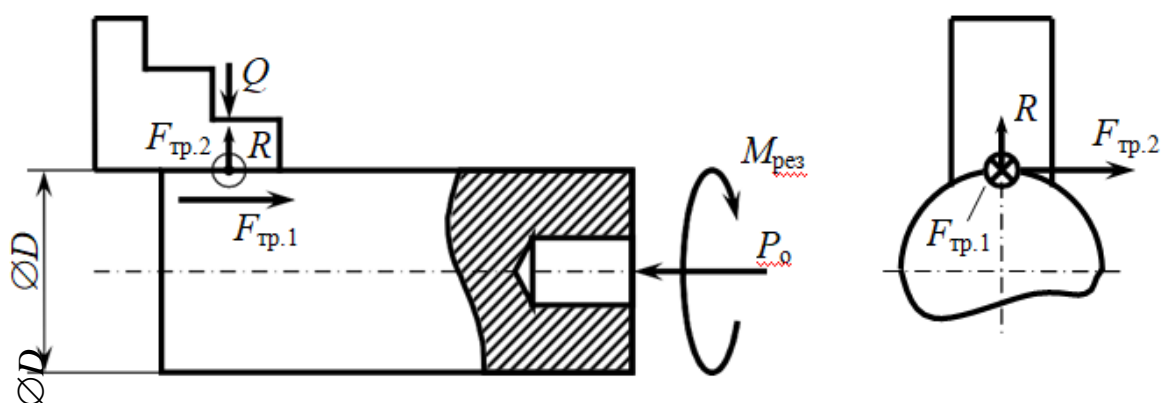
Схема к определению силы закрепления заготовки при сверлении отверстия на токарном станке
